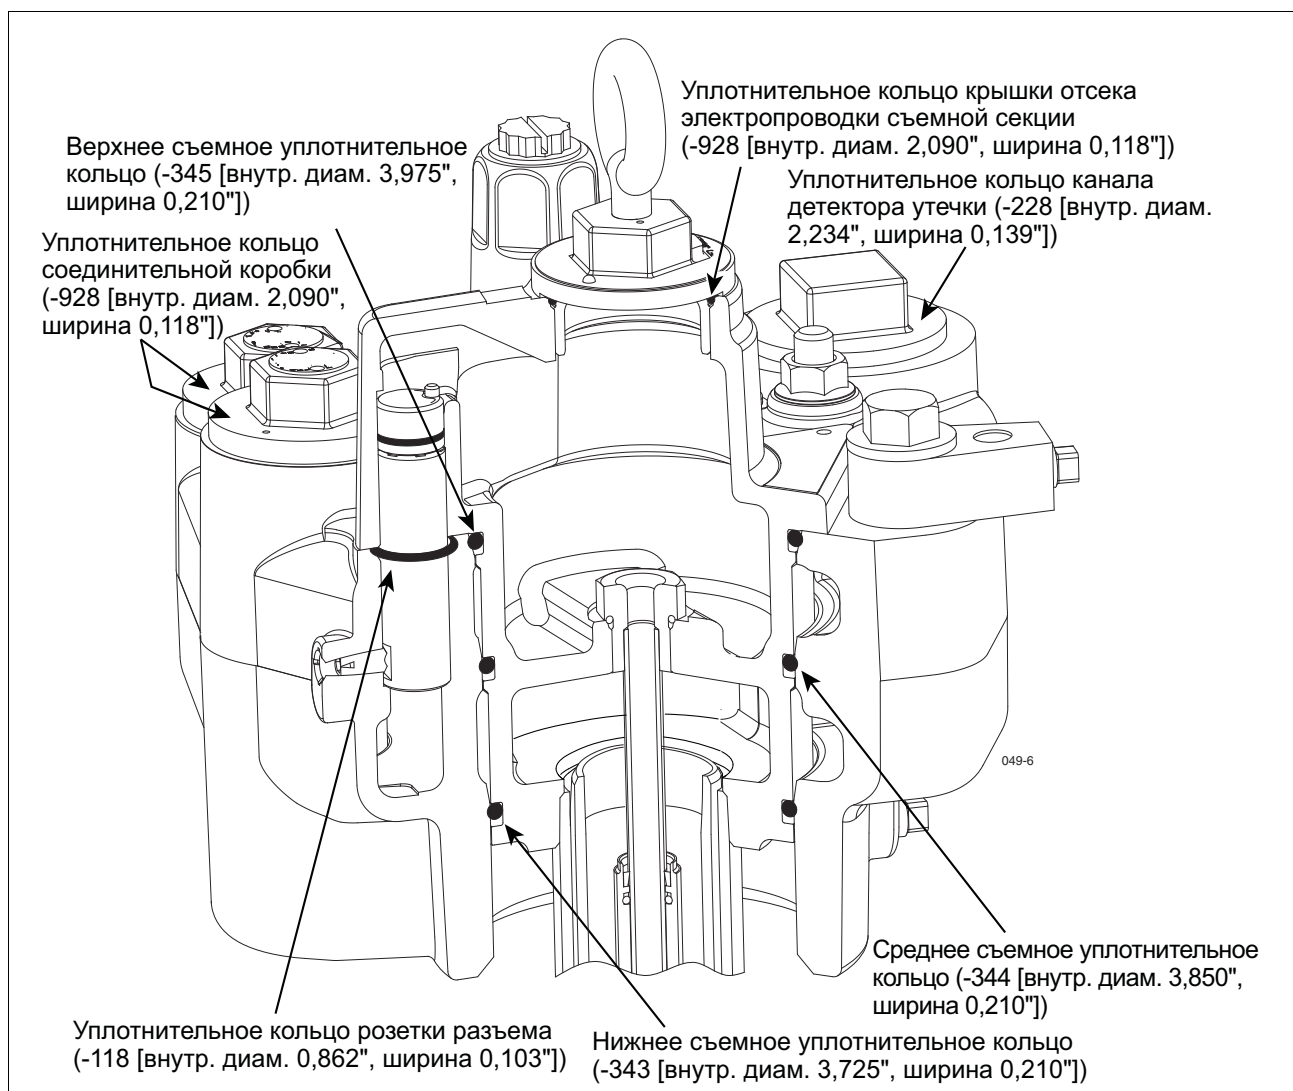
Местоположения уплотнительных колец пакера и манифольда
